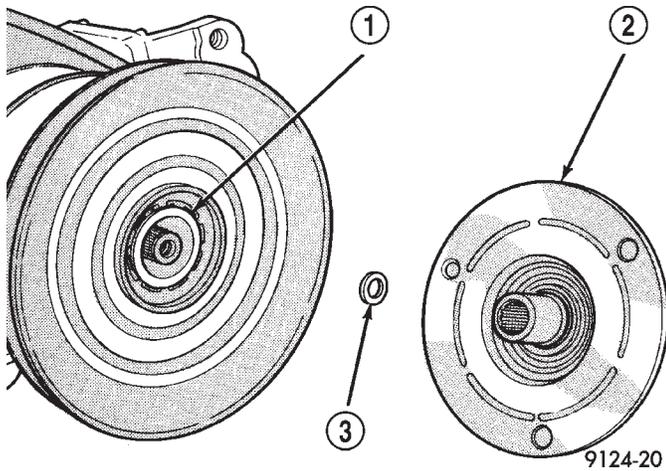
Befestigungsschraube der Kompressorwelle
